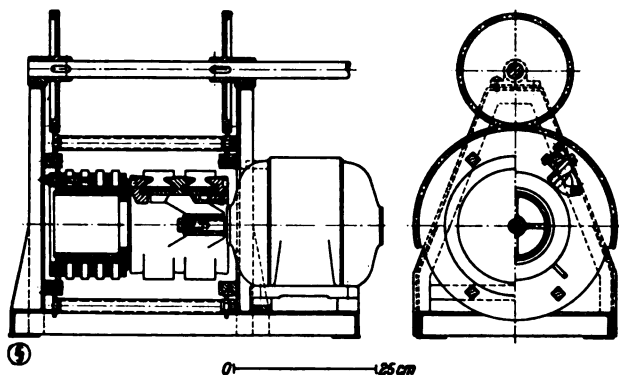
Gesteuerter Quecksilberdampf-Gleichrichter. Taktgeber für Lokomotivbetrieb.
